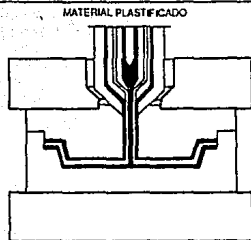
Moldeo por coinyección. (Ref. 26).
